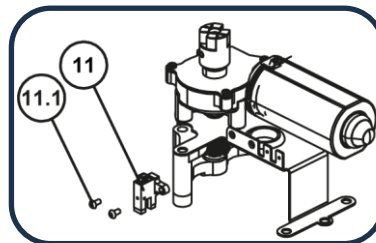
Engine unit pan or tilt mit Positioning sensor kit
